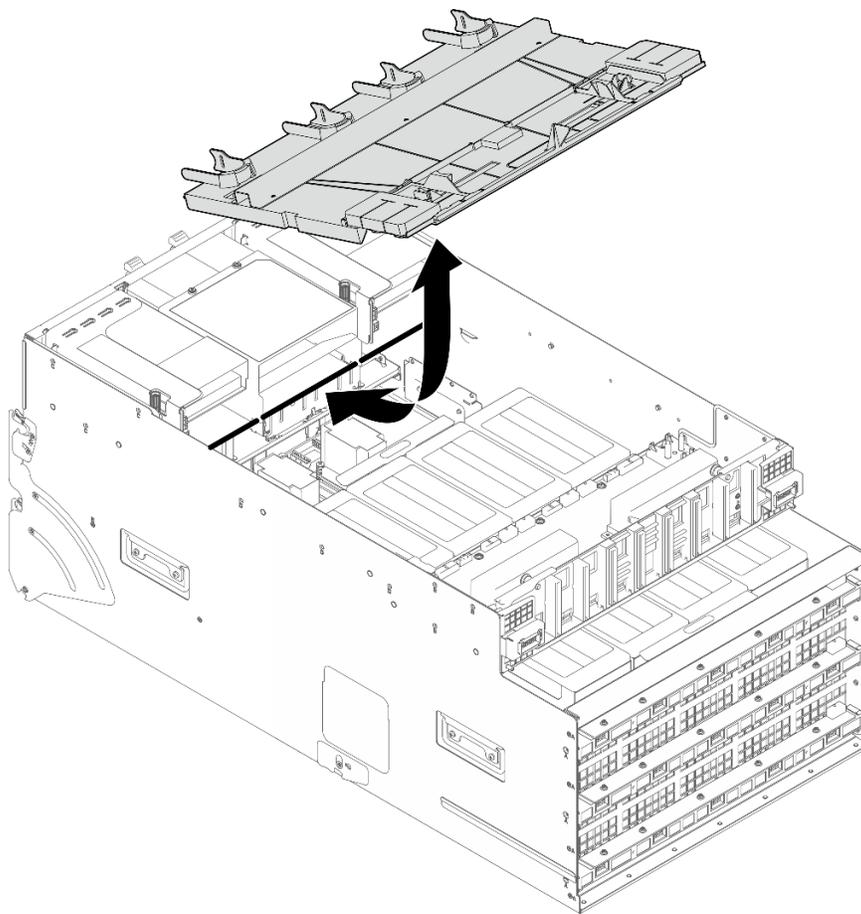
Remoção da estrutura do suporte do cabo e do conjunto do defletor
